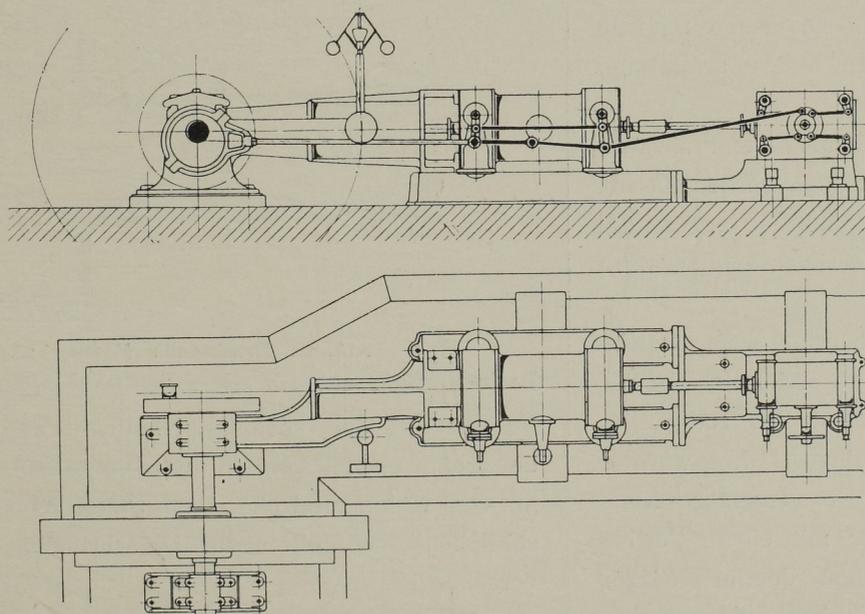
Seitenansicht und Grundriss. Massst. 1:80.
